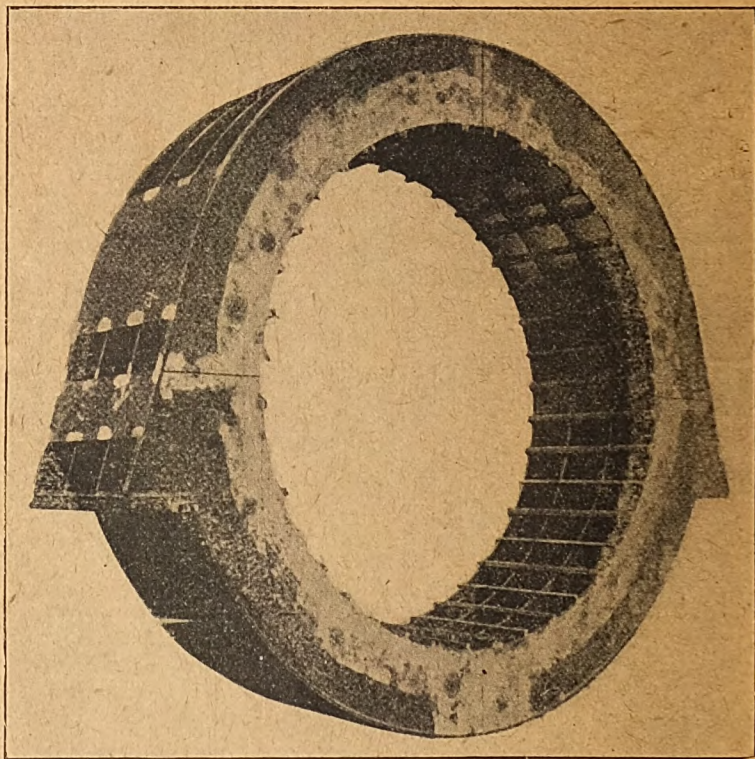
Carcasse d'un alternateur synchrone de 6 m de diamètre, entièrement construite par soudure suivant schéma n° 3.
